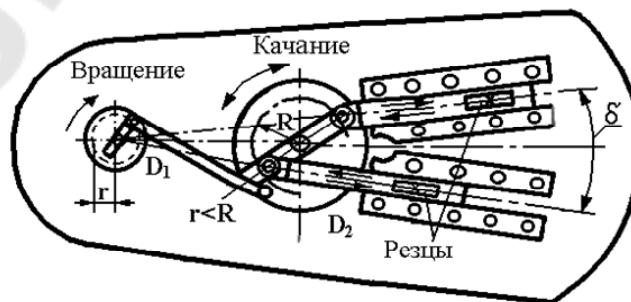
Схема кривошипно-шатунного механизма станка модели 526
